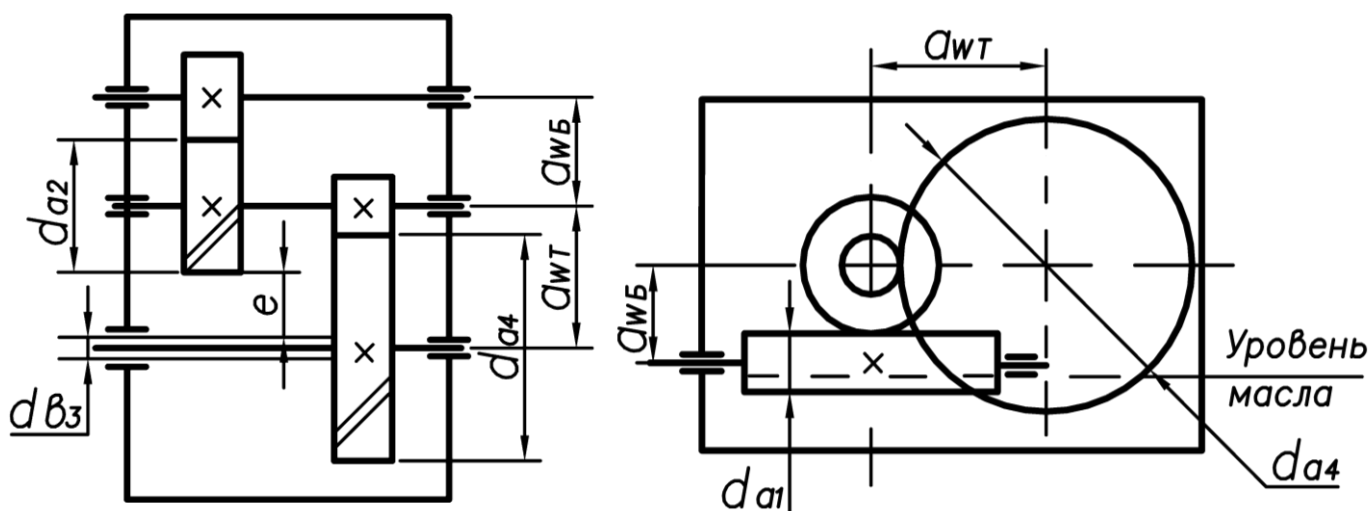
Схема двухступенчатого косозубого редуктора
